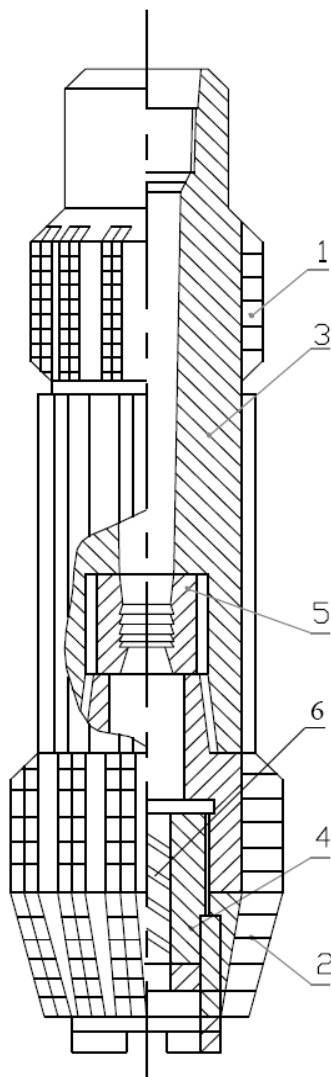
Фрезер-райбер усовершенствованной конструкции:
